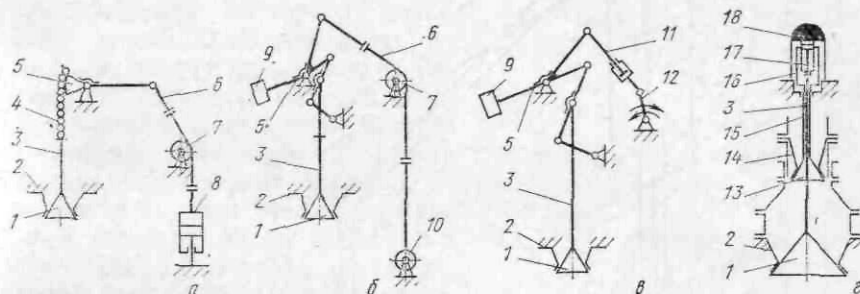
Схемы привода конусов загрузочного устройства: а — свободное опускание конусов; б, в, г — принудительное опускание конусов; 1 — большой конус; 2 — чаша; 3 — штанга большого конуса; 4 — цепь; 5 — балансир; 6 — канат; 7 — блок канатный; 8 — пневматический цилиндр; 9 — контргруз; 10 — электрическая лебедка; 11 — шатун; 12 — кривошип; 13 — малый конус; 14 — воронка малого конуса; 15 — штанга малого конуса; 16 — гидравлический цилиндр малого конуса; 17 — то же, большого конуса; 18 — рама
